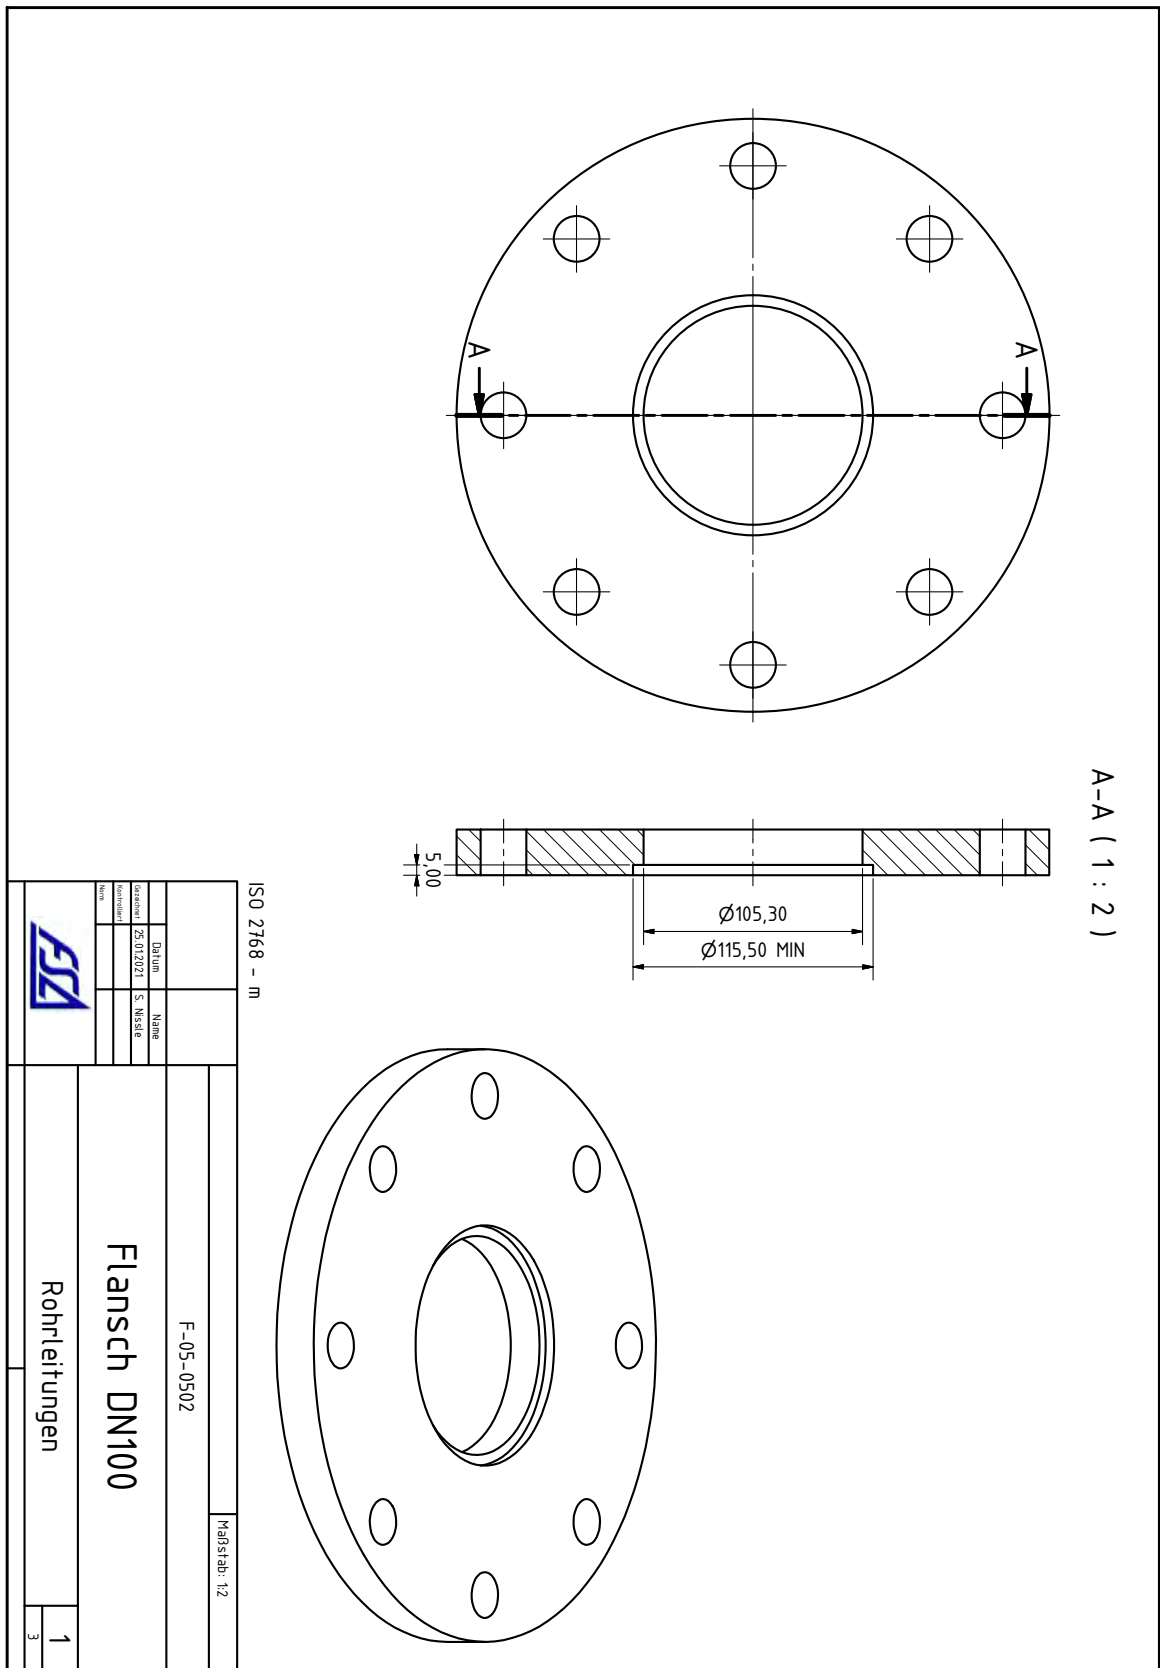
Konstruktionszeichnung Flansch DN 100 [20].
